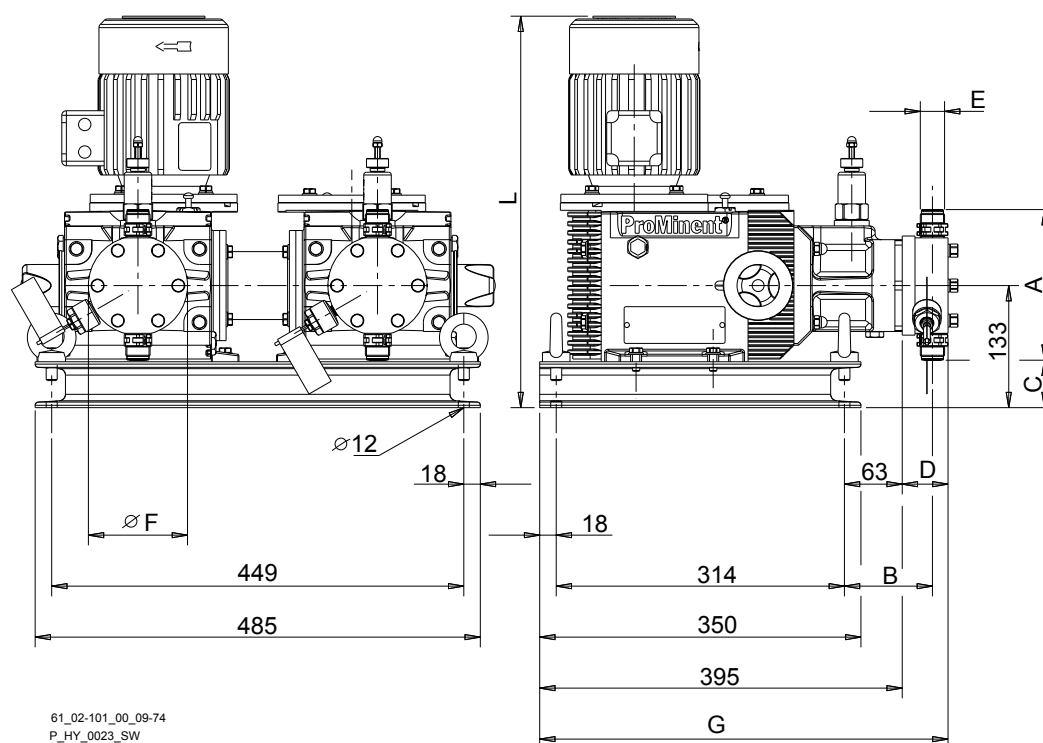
Hoja de dimensiones Hydro HP2 con accionamiento montado (HP2a E + HP2a A) - Dimensiones en mm
